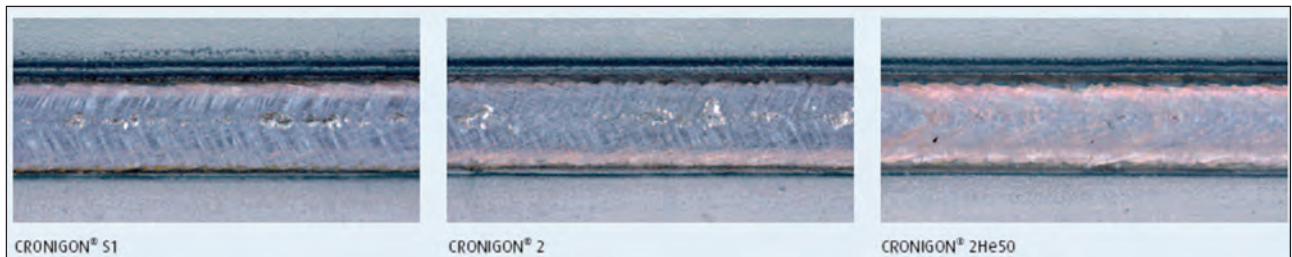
Образцы, полученные сваркой неплавящимся электродом в различных защитных газовых смесях
